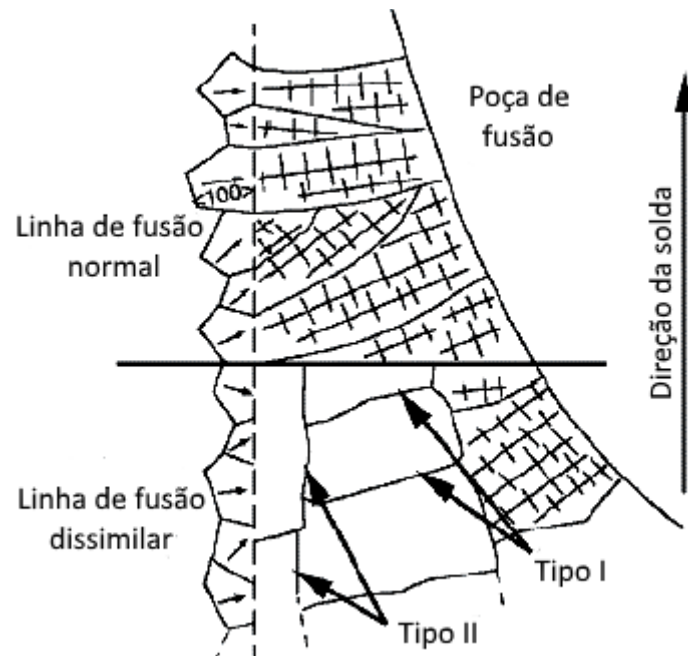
Representação dos contornos de grão em uma solda similar e dissimilar, com metal de adição austenítico e metal base ferrítico [26].
